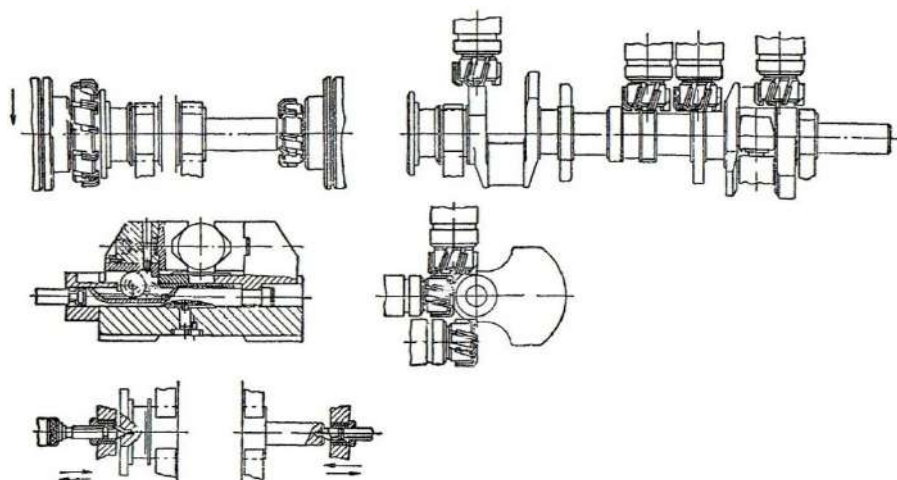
Обробка настановних площадок на штоках і центрування колінчастих валів на фрезерно-центрувальному напівавтоматі
